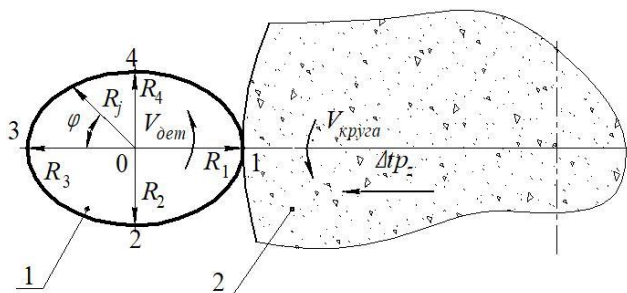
Начало процесса шлифования с момента касания круга наибольшим радиусом R_1 эллипсной заготовки: 1 – заготовка с эллипсным профилем; 2 – шлифовальный круг
